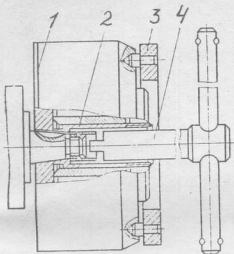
Отворачивание гайки крепления муфты опережения впрыска топлива:
